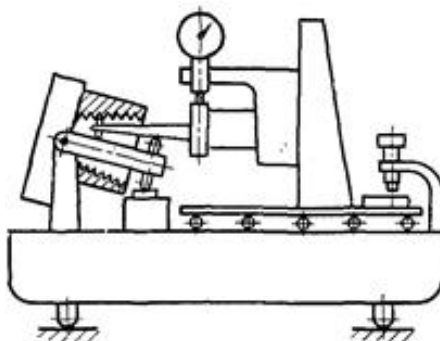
Схема измерения шага резьбы калибра-кольца прибором 481К (481КМ)
